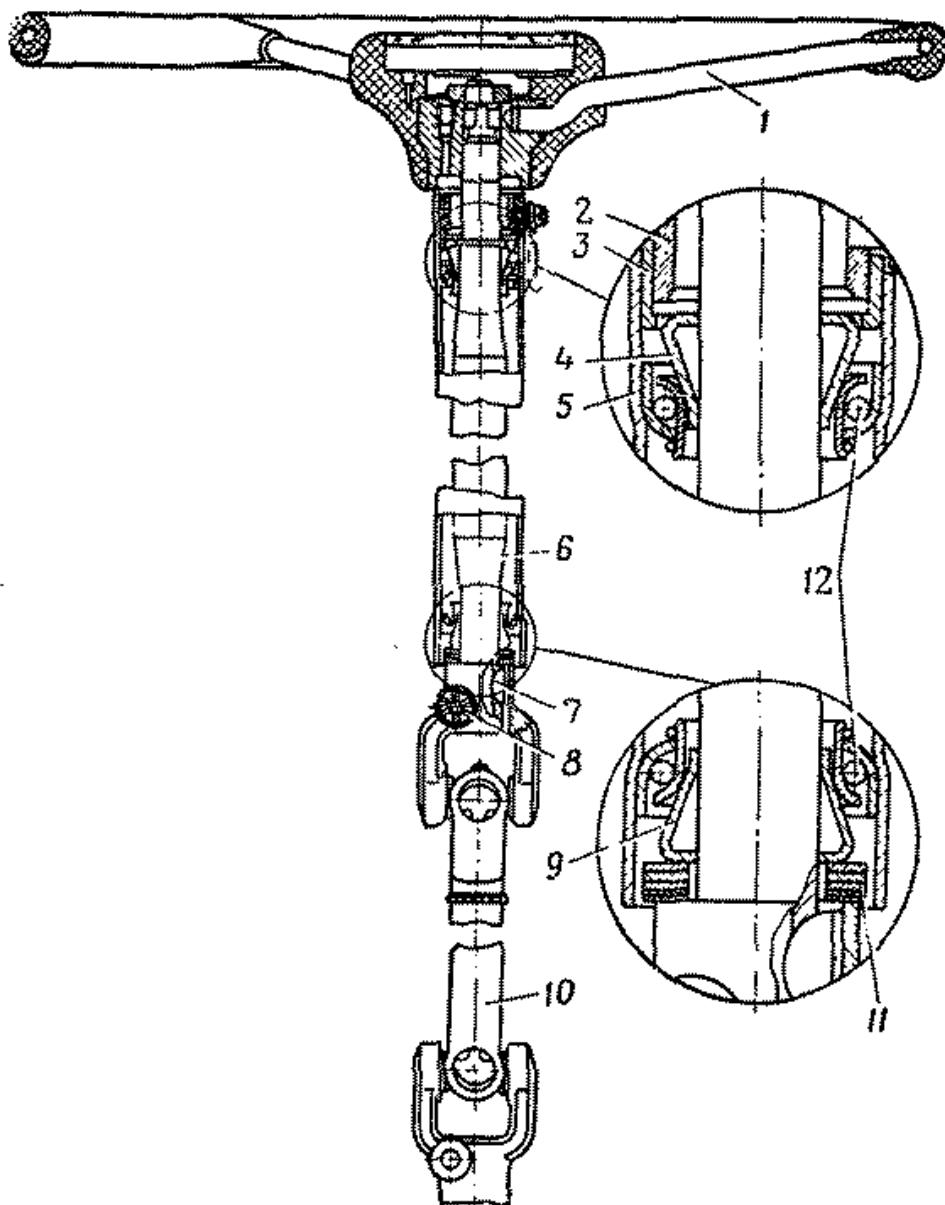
Рулевая колонка в сборе с рулевым колесом:
